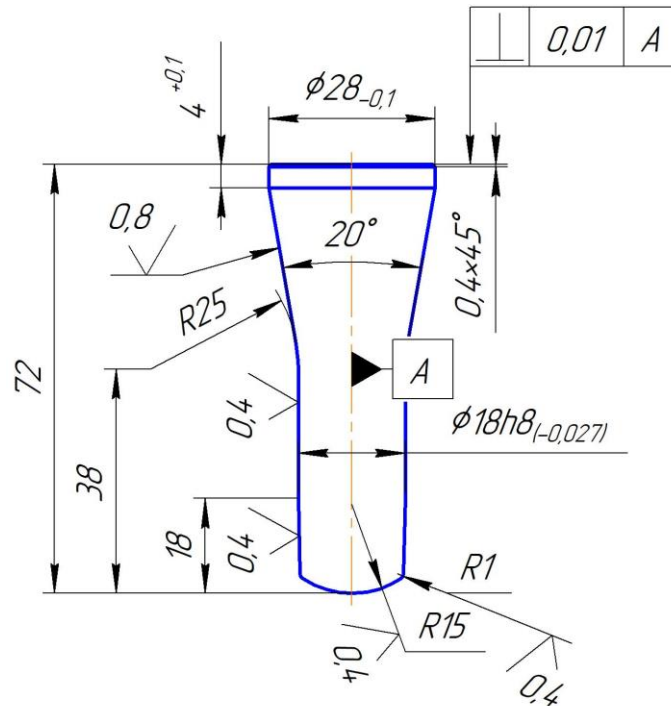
Пуансон для холодного зворотного видавлювання деталі «Втулка».
